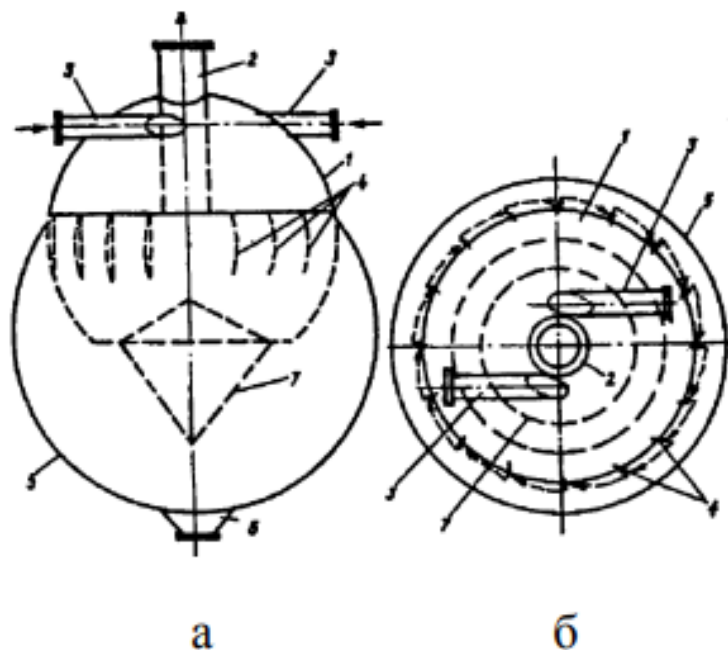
Сферичний циклон: а – вид збоку; б – вид зверху.
